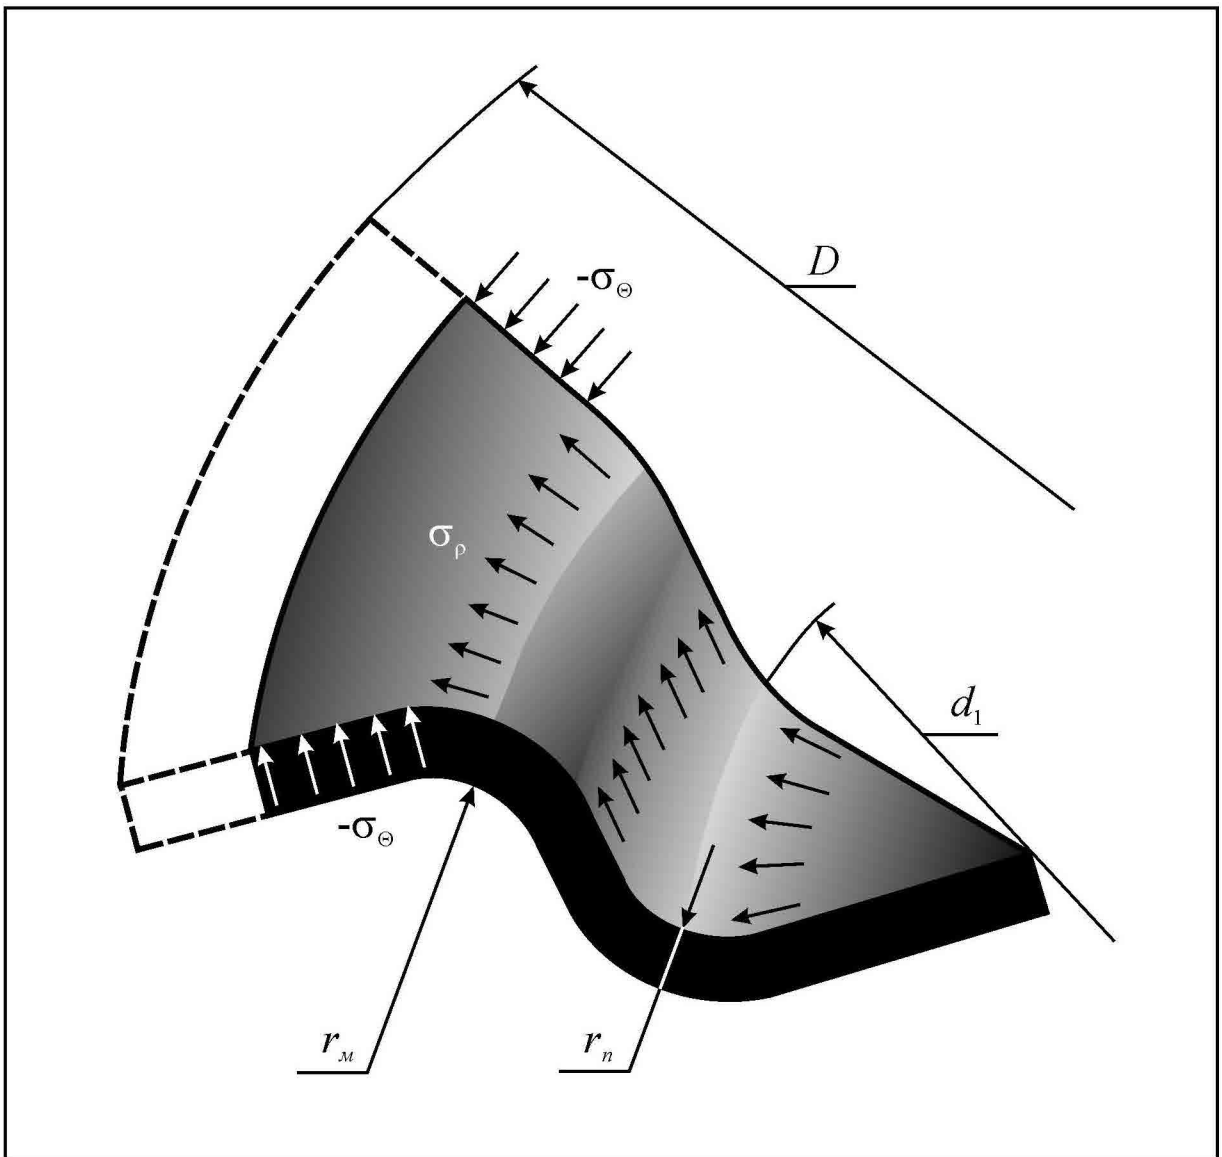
Напруження, що виникають в різних частинах заготовки при витягуванні з притиском фланцю
